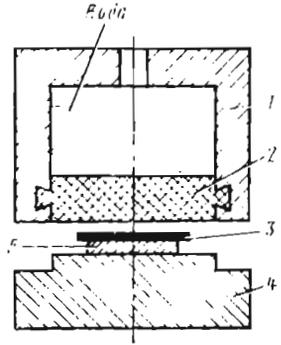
Оснастка для формовки гидроэластичной средой:
